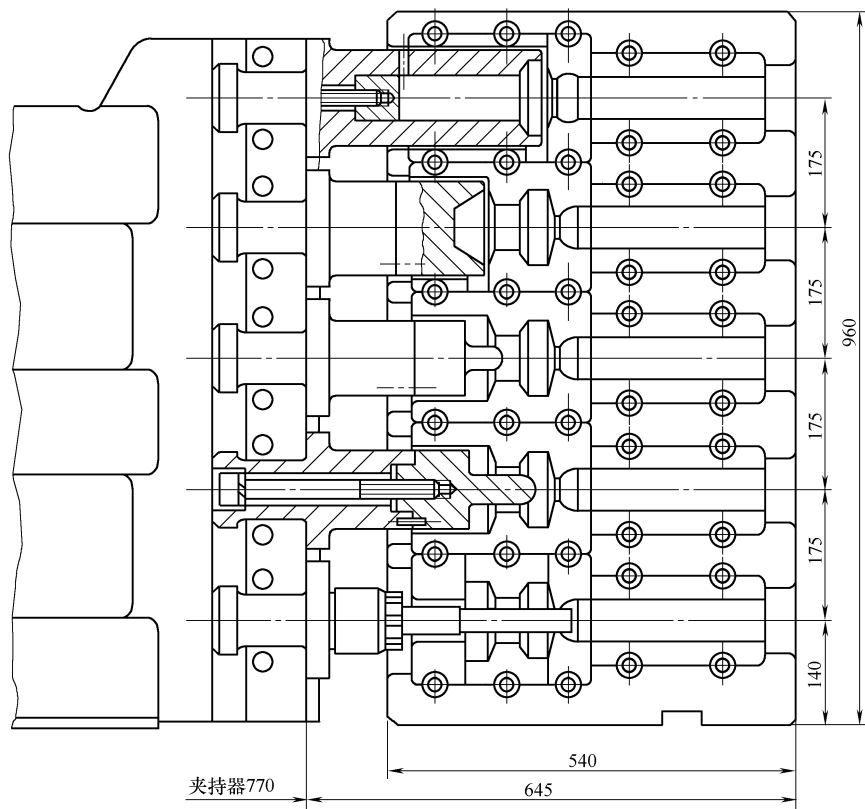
倒车齿轮 12500kN 垂直分模平锻机模具
